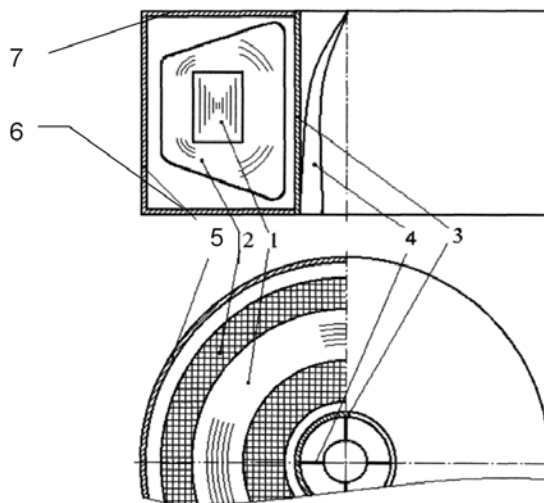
Однофазный тороидальный нагревательный элемент
